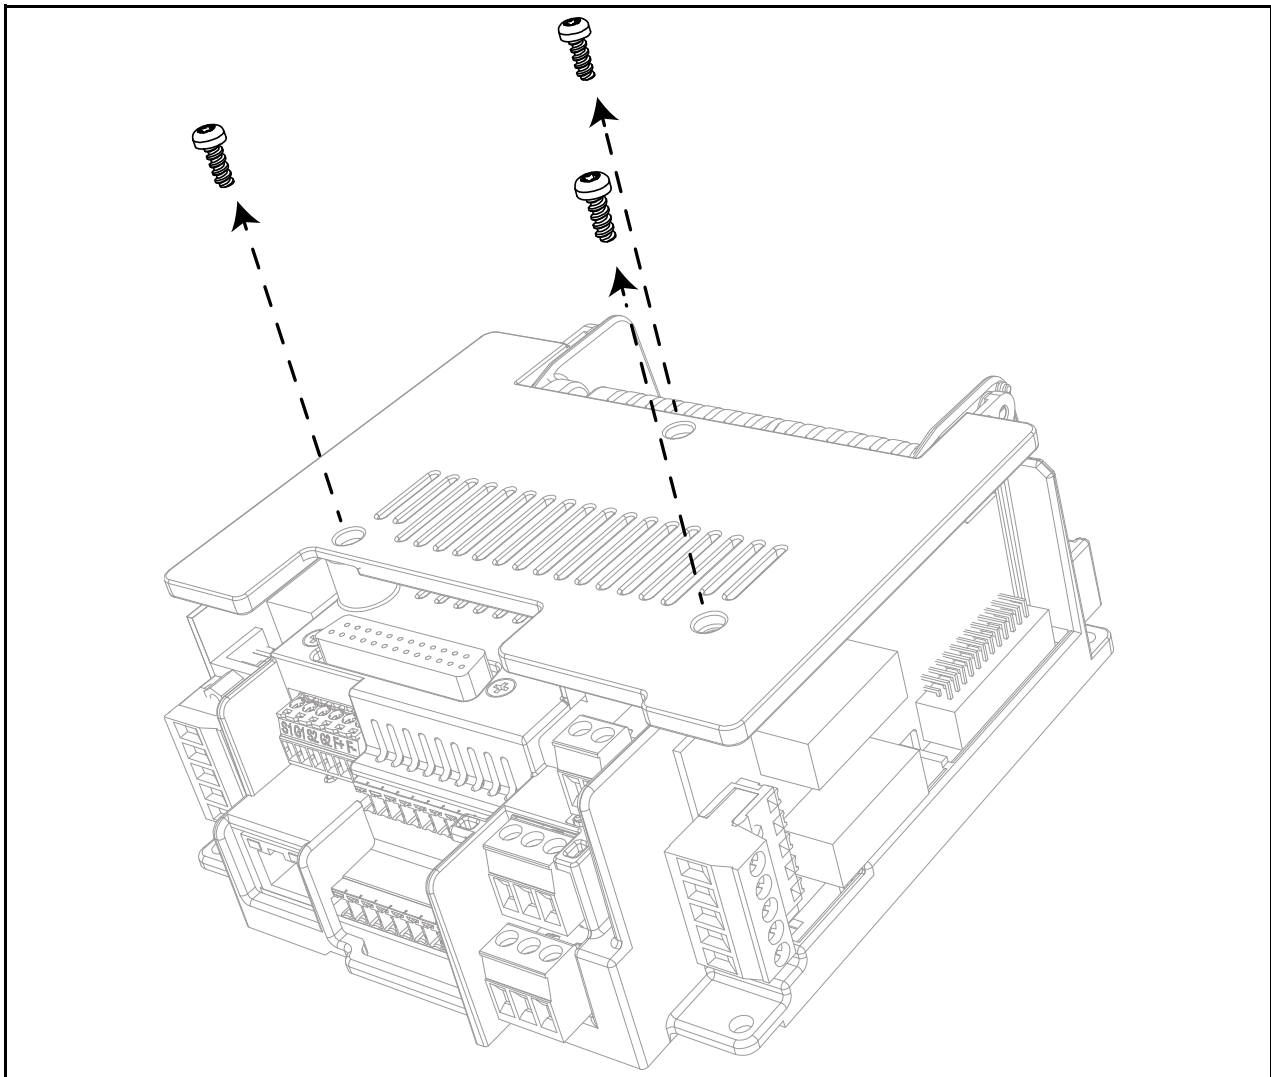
Entfernen Sie die drei Schrauben des Steuerkastens.
